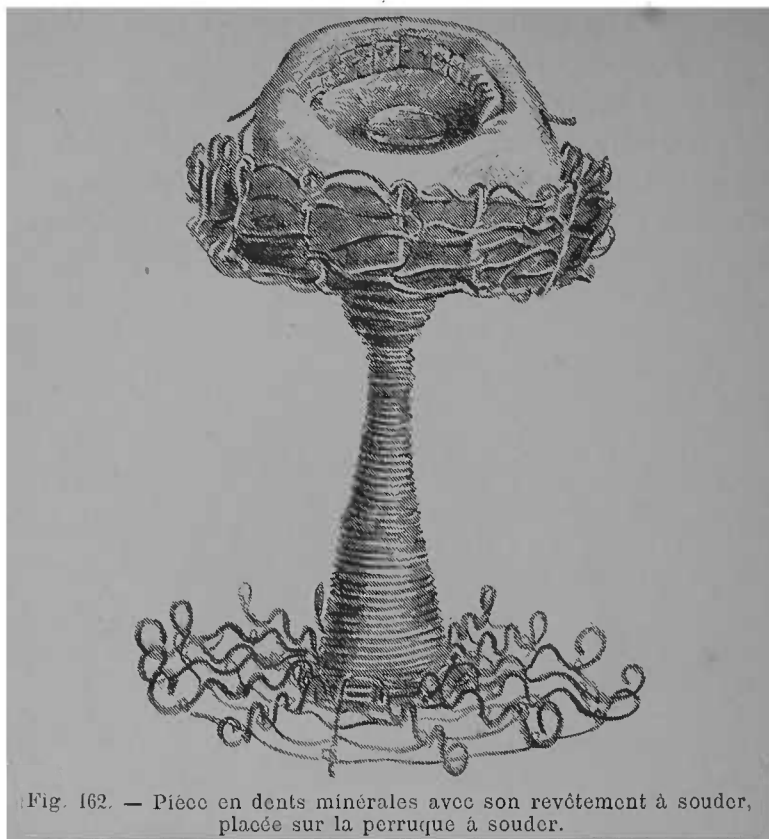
Pièce en dents minérales avec son revêtement à souder, placée sur la perruque à souder.
